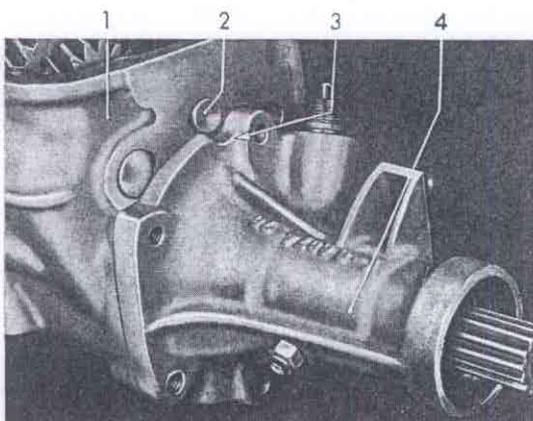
Getriebegehäuseverlängerung um Hauptwelle gedreht, bis Achse für Nebenwellen-Zahnradblock freiliegt
